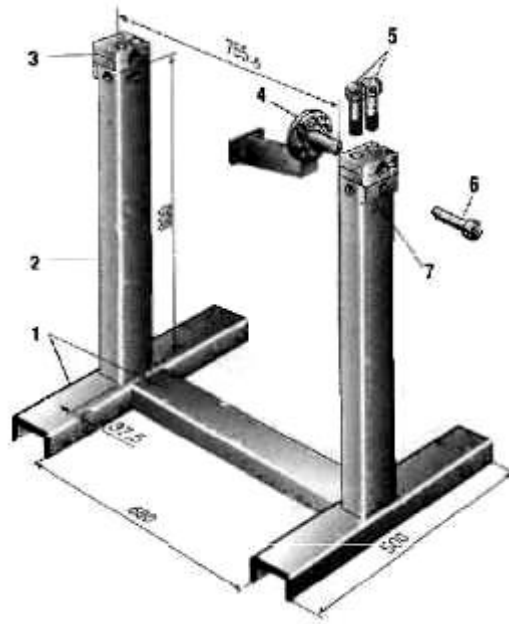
Універсальний стенд для розбирання - складання мостів: 1 – основа; 2 – стійка (2 шт.); 3 – підшипник (2 шт.); 4 – опора; 5 – болт (4 шт.); 6 – палець-фіксатор (2 шт.); 7 – накладка (2 шт.)
